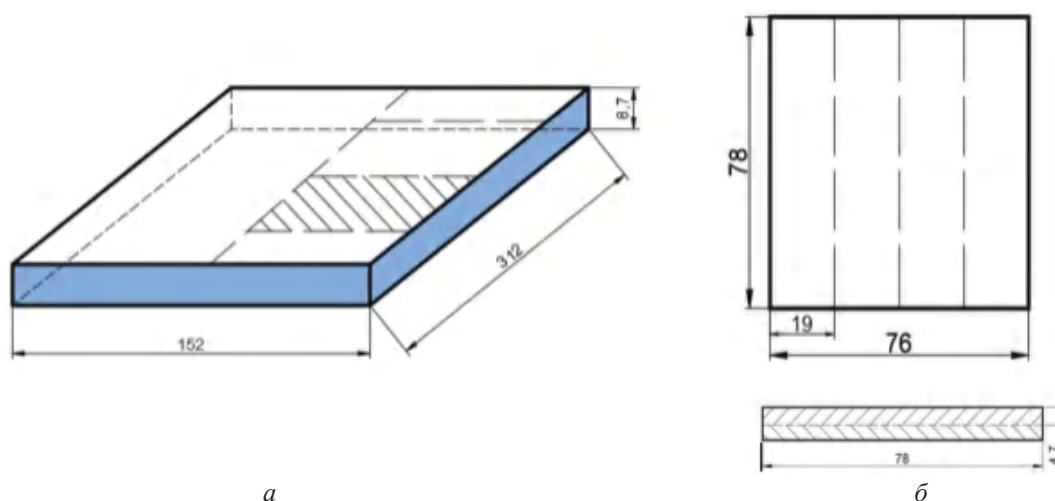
Схема вырезки образца из сваренного взрывом СКМ (а) и подготовка образцов для прокатки (б)
